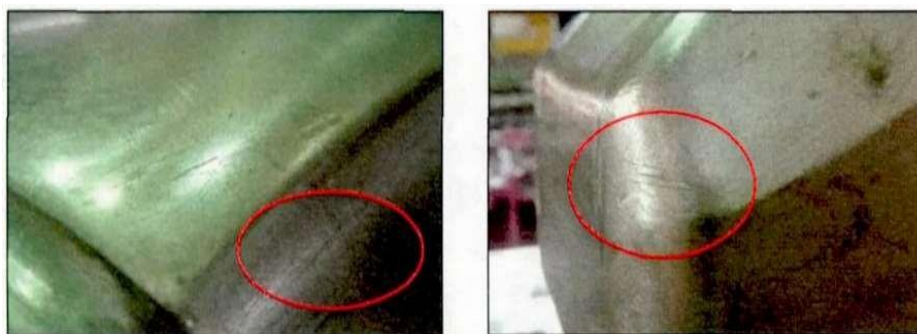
Дефекты на рабочих поверхностях инструмента [87]
